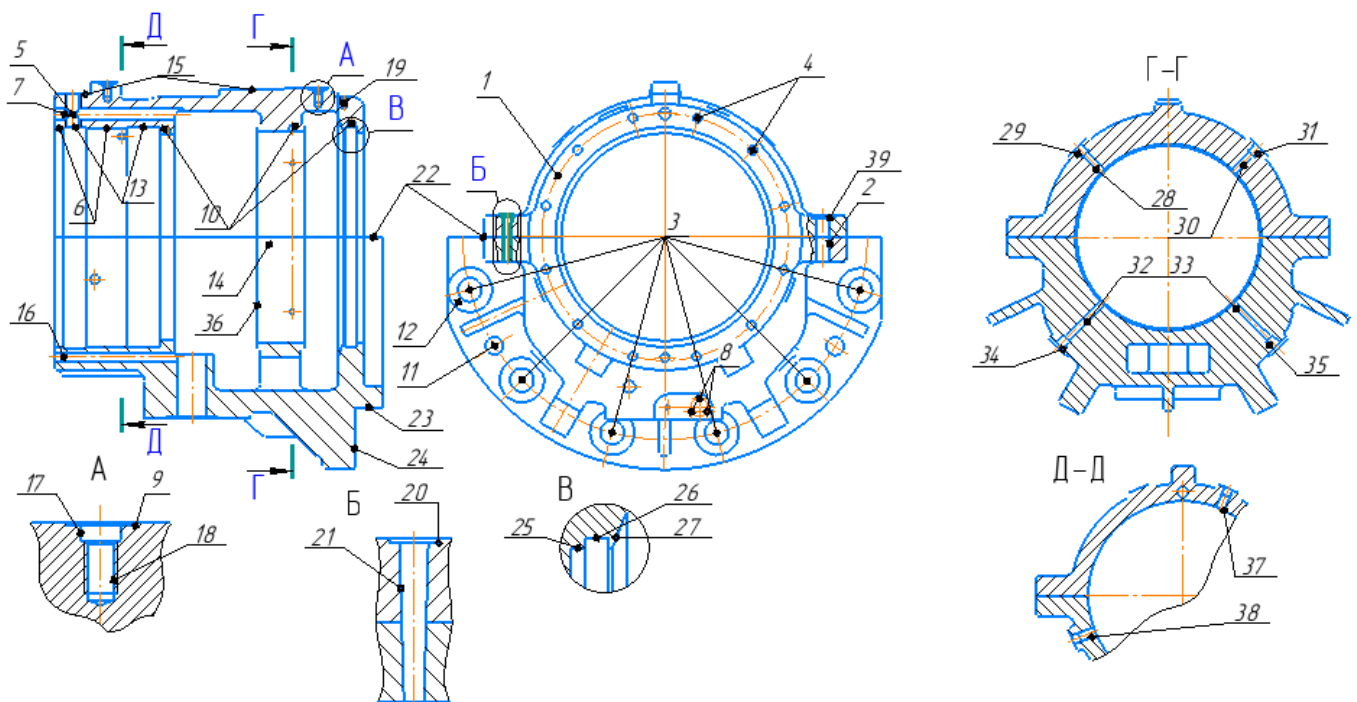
Чертеж детали «Корпус радиально-упорного подшипника»
